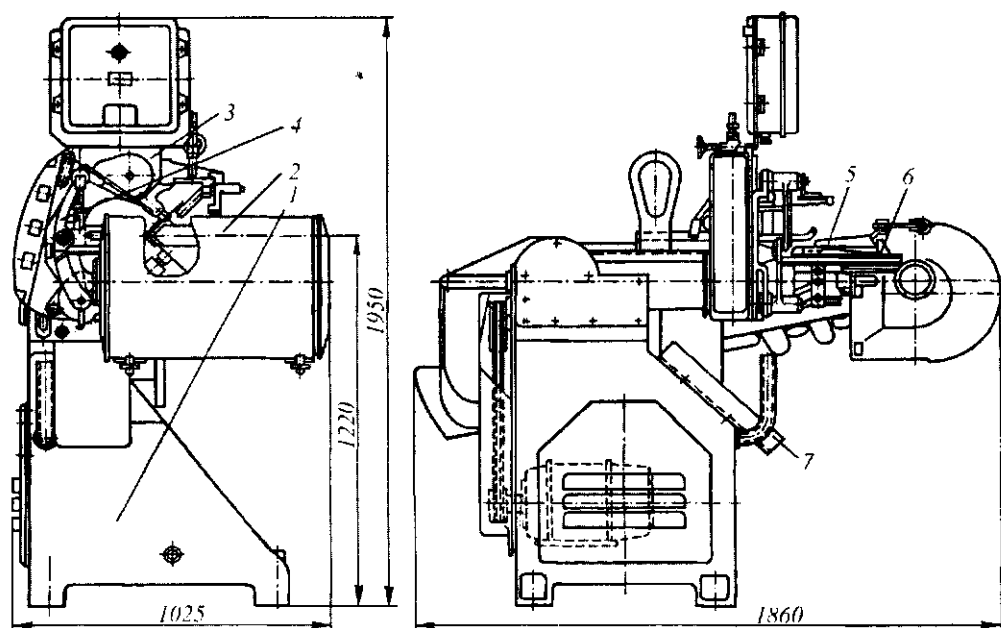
Машина А8-ИТО для обезглавливания тресковых рыб
